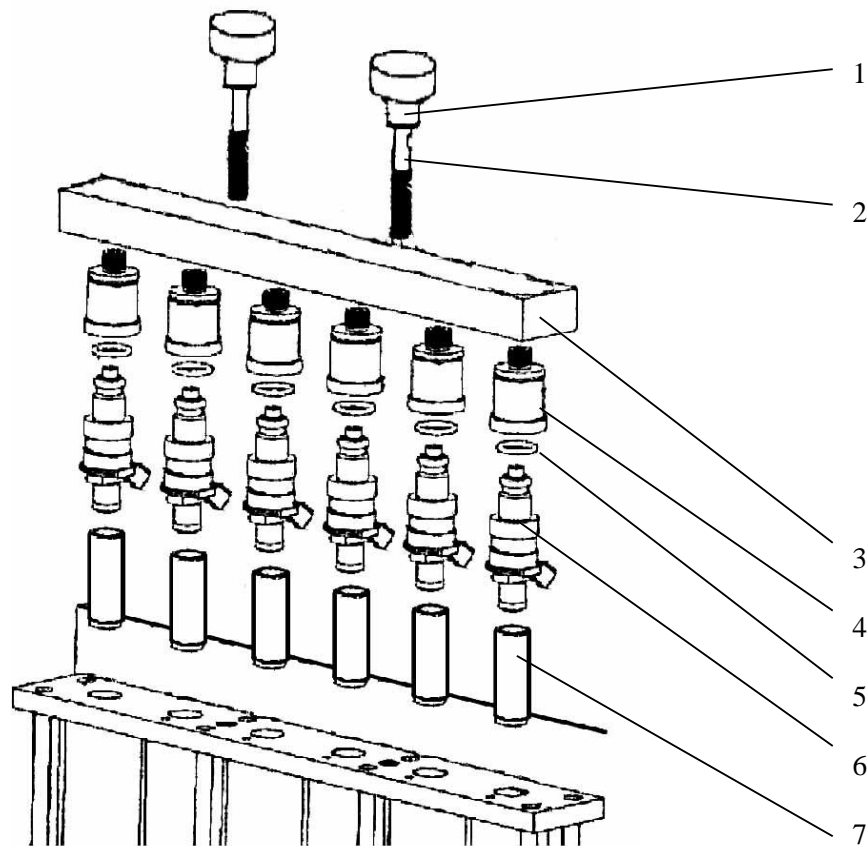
Схема установки форсунок при обратной промывке: 1 - гайка крепления рамп; 2 – шпилька; 3 – раampa; 4 – переходник; 5 – уплотнительное кольцо; 6 – форсунка; 7 – проставка.
